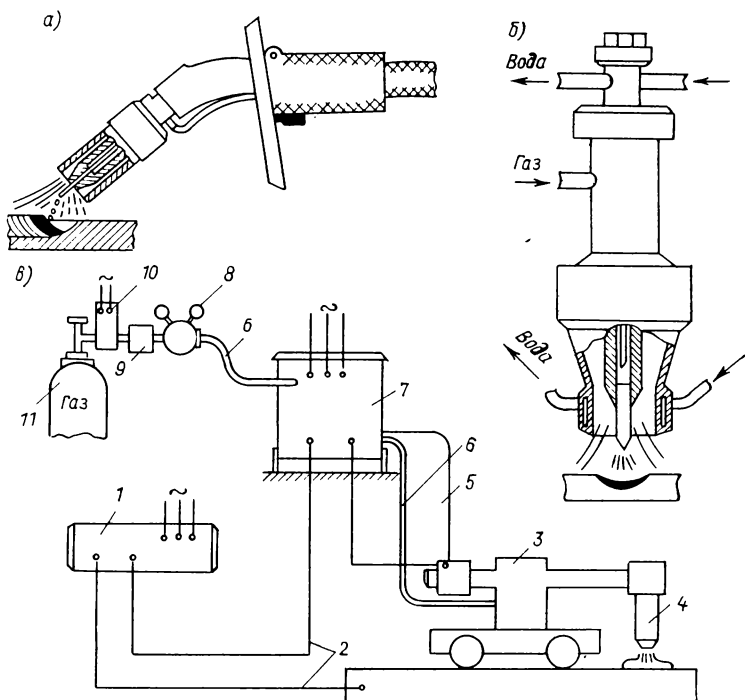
Схема установки для сварки в защитных газах; а — пистолет для полуавтоматической сварки плавящимся электродом; б — горелка для сварки неплавящимся вольфрамовым электродом; в — общая компоновка установки для автоматической сварки.
